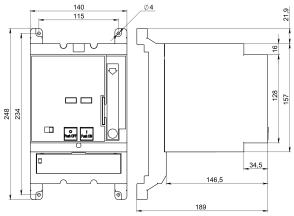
Габаритные и установочные размеры приводов ESMO T400-T630
